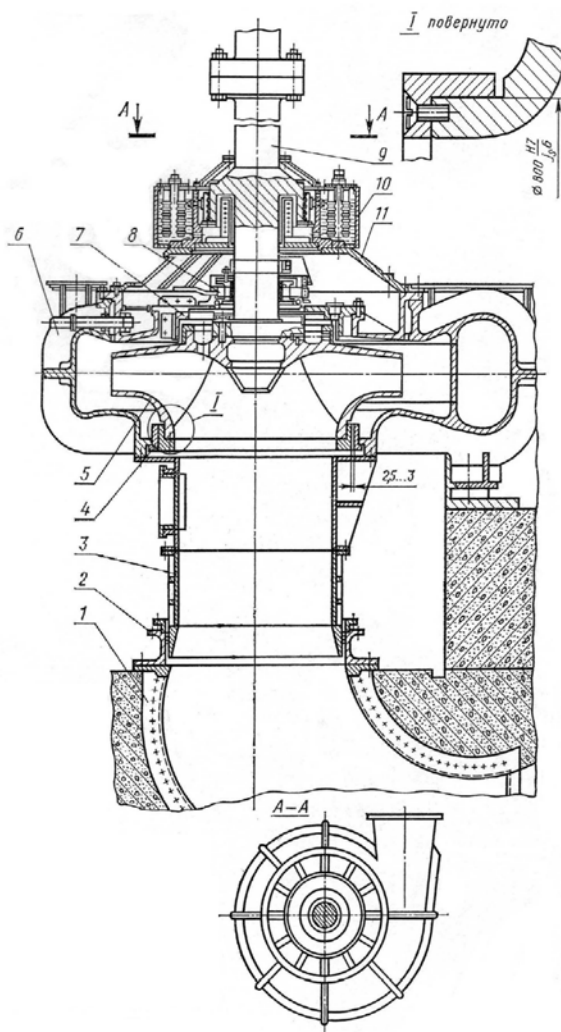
Насос центробежный типа В: 1 – колено подвода; 2 – опорное кольцо; 3 – проставка; 4 – переднее уплотнение рабочего колеса щелевого типа; 5 – рабочее колесо; 6 – корпус насоса; 7 – верхнее щелевое уплотнение рабочего колеса; 8 – подшипник скольжения; 9 – фланец; 10 – корпус радиального подшипника; 11 – крышка
